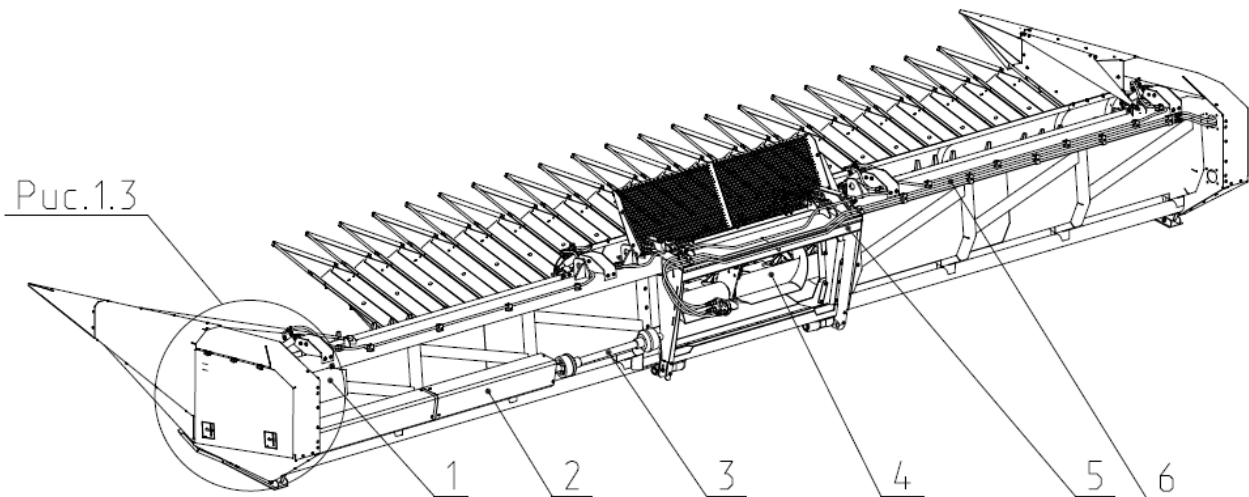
Общий вид жатки ЖНП-9,5 ПГ
